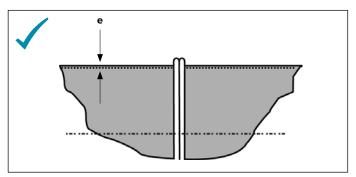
Schweißnaht mit gleichmäßige Wulstausbildung (gut)
